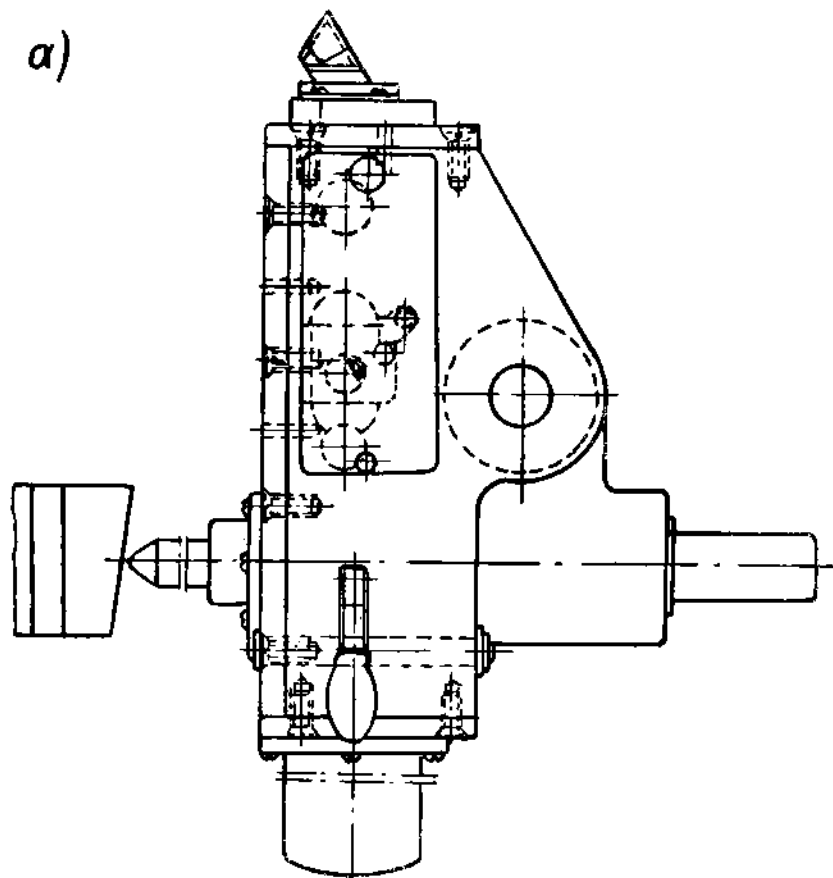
Резец Ю. Дикого и Н. Чикирева для скоростного нарезания многоходовой резьбы
